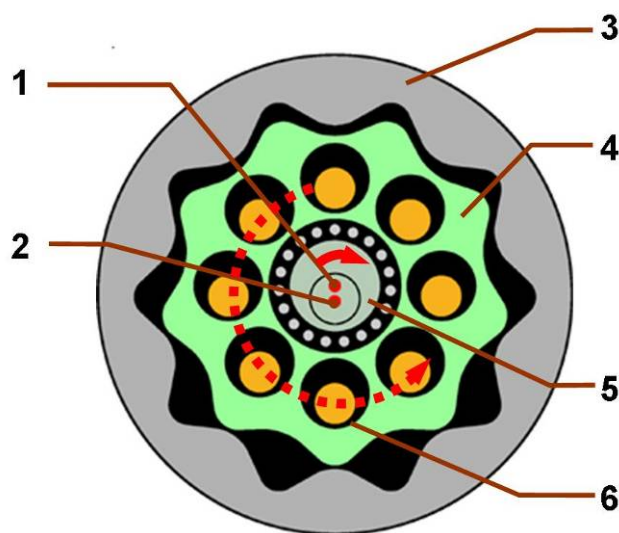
Редуктор механизма переключения рычага: 1 - центр эксцентриковой пластины; 2 - центр первичного вала электродвигателя механизма переключения; 3 - внутренняя шестерня (61 зуб); 4 - наружная шестерня (60 зубьев); 5 - эксцентриковая пластина; 6 - вторичный вал
